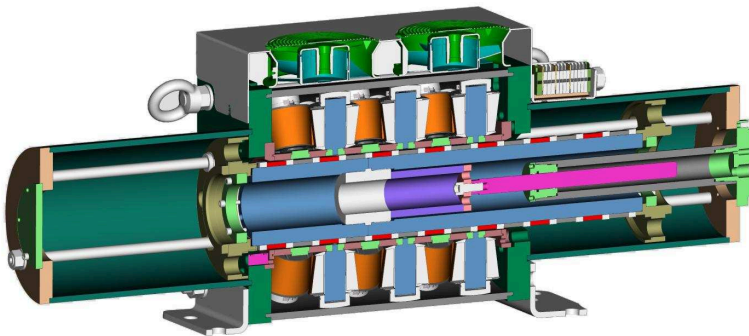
CAD-Zeichnung des Linearmotors
